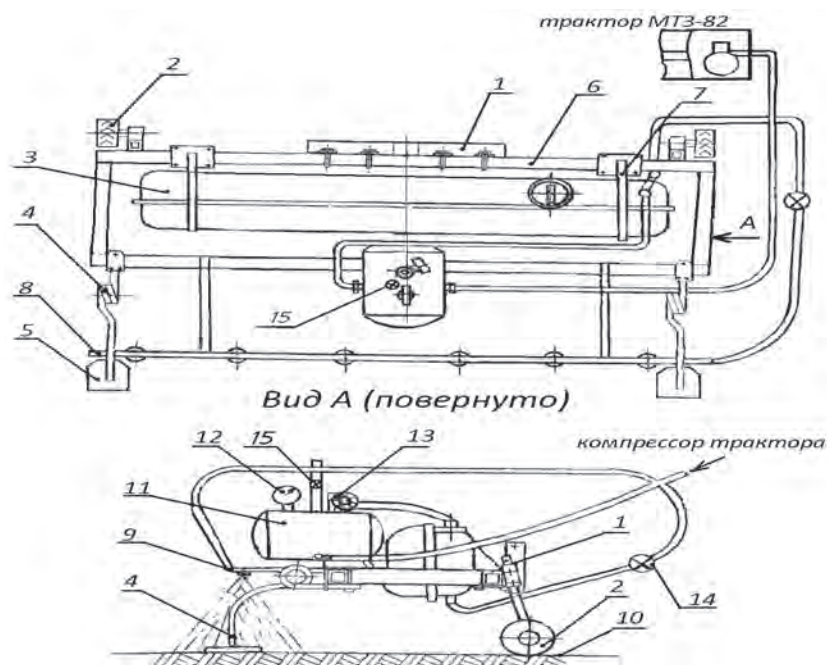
Принципиальная схема машины для внесения жидких удобрений на горные луга и пастбища: 1 – замок автосцепки; 2 – опорные колеса; 3 – цистерна; 4 – пружинистая стойка; 5 – дополнительная опора; 6 – рама; 7 – кронштейн крепления цистерны; 8 – коллектор распылителей; 9 – распылитель; 10 – почва; 11 – ресивер; 12 – манометр; 13 – клапан редуционный; 14 – кран управления, 15 – кран спуска воздуха
